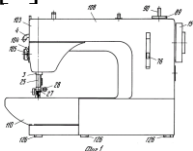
Общий вид бытовой швейной машины, представленной в патенте RU2091526
